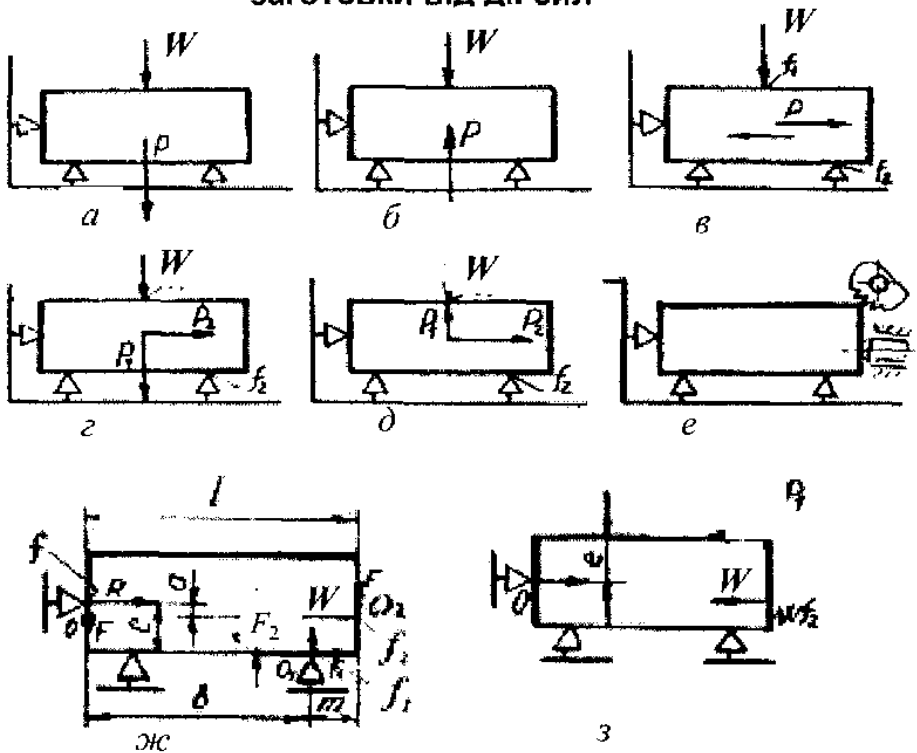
Розрахункові схеми для визначення затискних зусиль заготовки від зміщення
